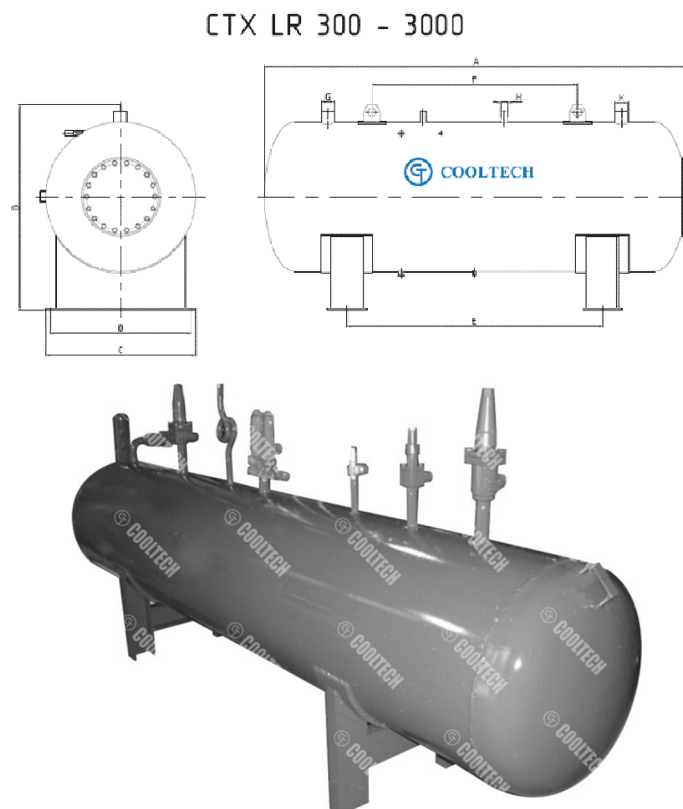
Горизонтальний ресивер COOLTECH CTXLR
